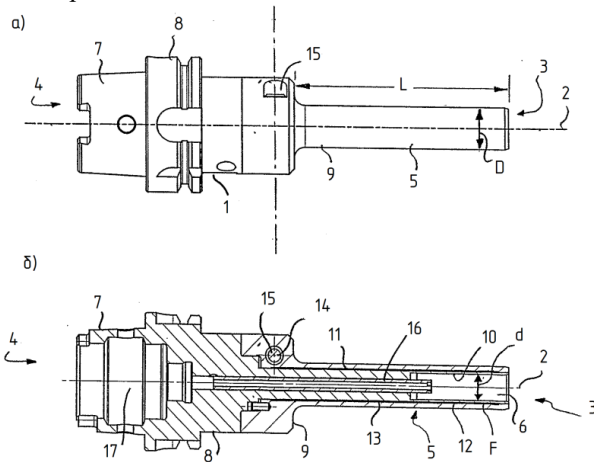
Гидравлический расширительный патрон: а – вид сбоку, б – продольный разрез, 1 – ударная поверхность, 2 – ось, 3 – конец патрона со стороны инструмента, 4 - конец патрона со стороны станка, 5 – шейка, 6 – приемник для инструмента, 7 – конус крепления, 8 – основной корпус, 9 – зажимная втулка, 10 – расширительная втулка, 11 – кольцевой зазор, 12 – барокамера, 13 – система подачи давления, 14 – блок создания давления, 15 – отверстие, 16 – цапфа, 17 – выходное отверстие, F – кольцевой зазор, D – наружный диаметр, d – внутренний диаметр, L – осевая длина шейки
